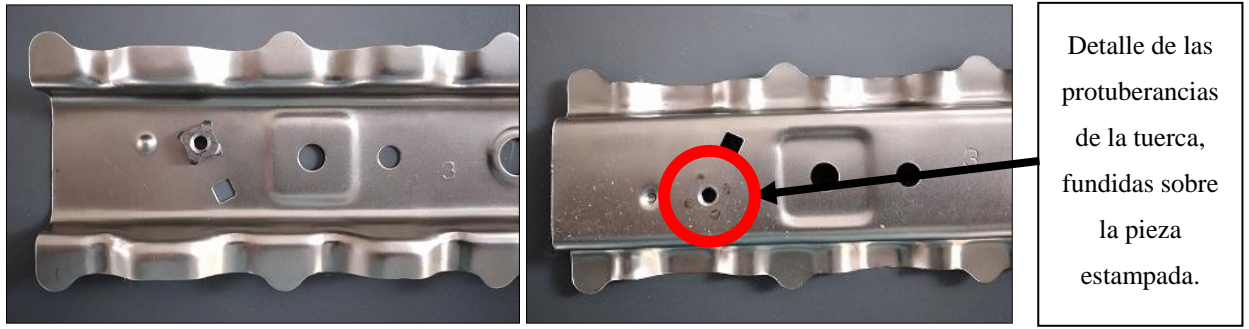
Vistas de una de las tuercas soldadas por proyección (anterior y posterior)
